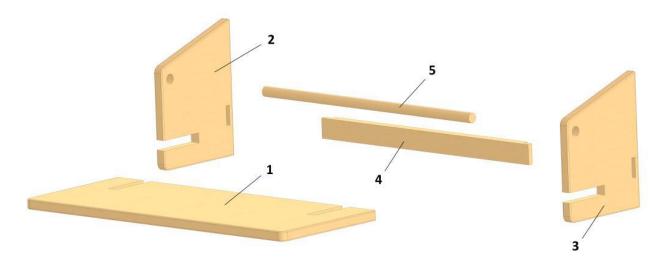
Упрощенный вид изделия – образец в разобранном виде:
